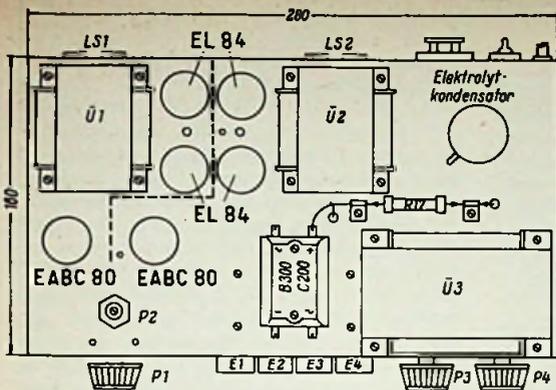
Montage-Skizze. Chassisgröße 280 X 160 X 70 mm; Material: 1,5 mm Aluminiumblech, einerseits abgebogen
